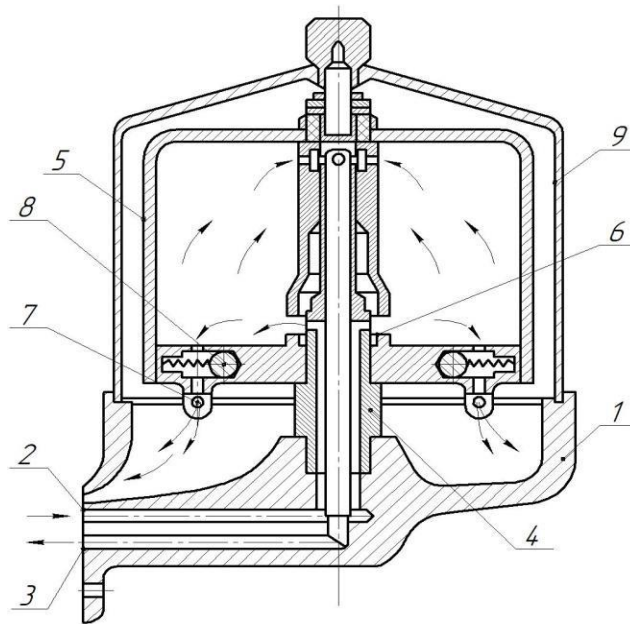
Схема центрифуга для очистки моторного мастила:
